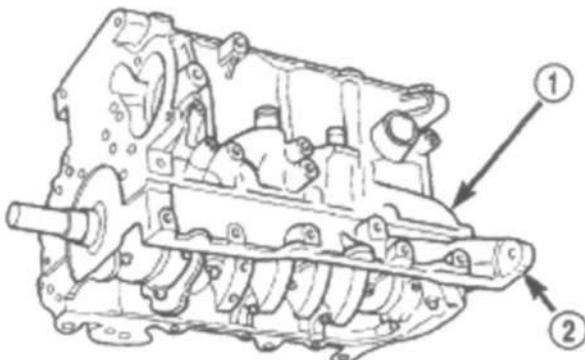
Блок цилиндров и основание двигателя 2.4L
